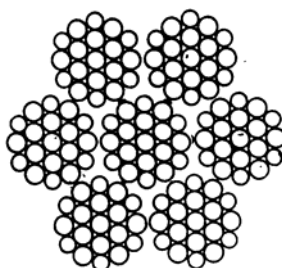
Поперечное сечение армирующих тросов для РТК (ТУ 14-285-159-92)
